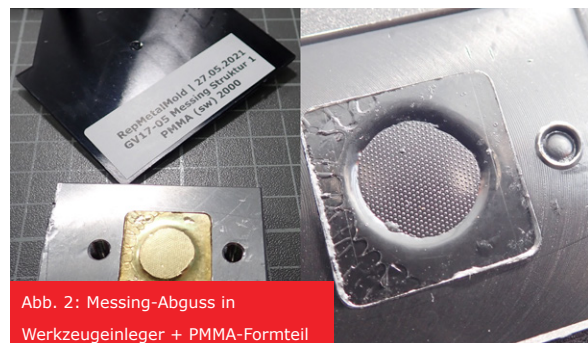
Messing-Abguss in Werkzeugeinleger + PMMA-Formteil
